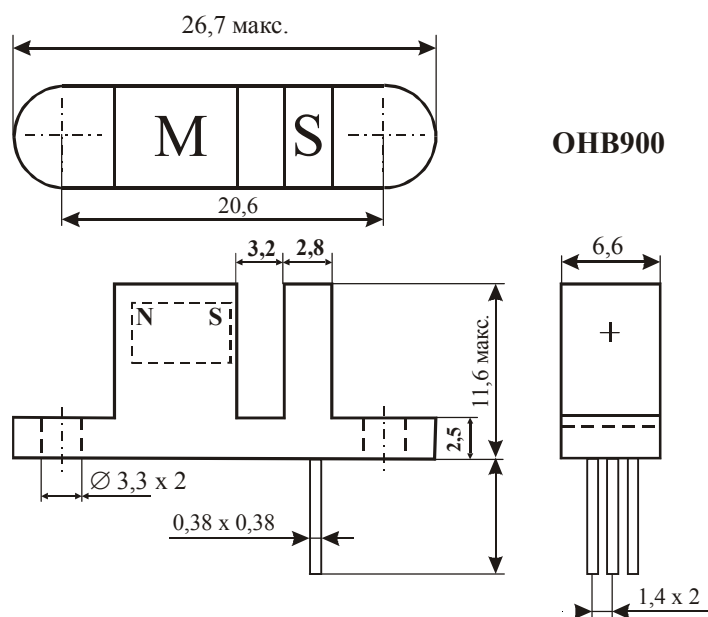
Внешний вид и габаритные размеры щелевого датчика серии OHB900, выпускаемого фирмой Optek Technology Inc.
